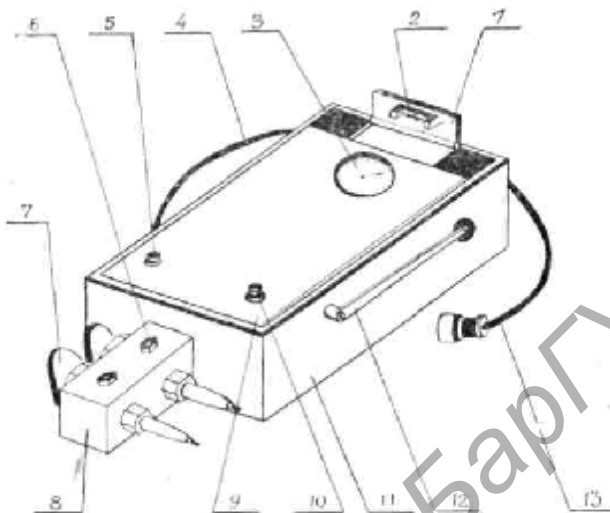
Приспособление Э-203-П для проверки свечей зажигания на искрообразование и герметичность
